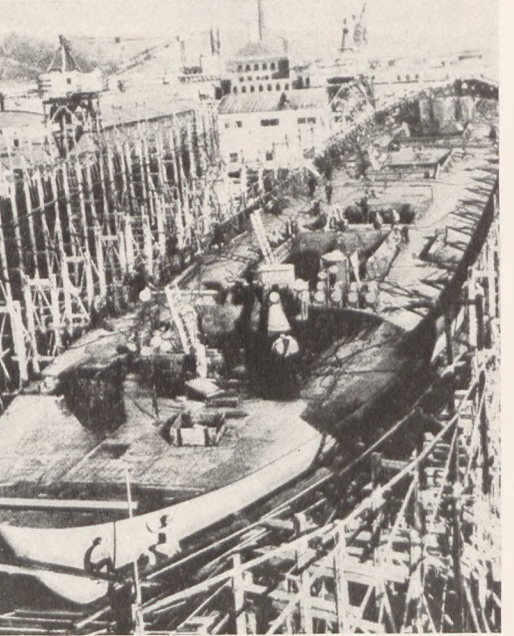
Ganzgeschweißtes Motorschiff des C 1-Typs Klasse „Cape Alava“, fertig bis zum Oberdeck.
